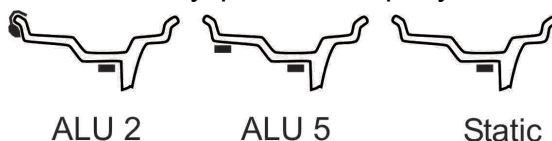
Схемы расположения грузов, для которых возможно прямое измерение для станков без второй линейки
